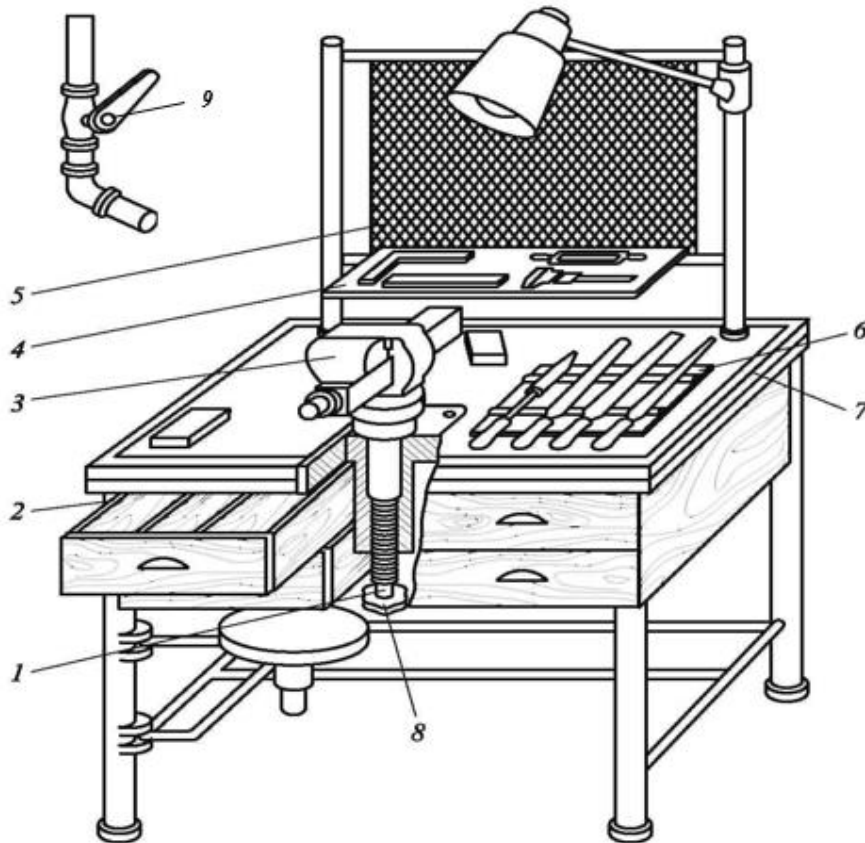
Одномісний слюсарний верстак: 1 - гвинт підйому і опускання регульованих лещат; 2 - ящик для інструменту; 3 - лещата плоскопаралельні; 4 - інструментальна полиця; 5 - захисний екран; 6 - планшет для інструменту; 7 - бортик із сталевого кутика; 8 - рукоятка приводу вертикального переміщення лещат; 9 – кран для подачі стиснутого повітря
